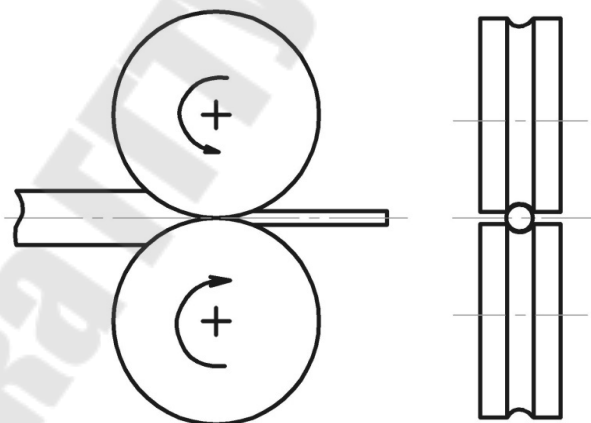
Схема роликовой волоки (ролик, проволочная заготовка, готовый профиль)
